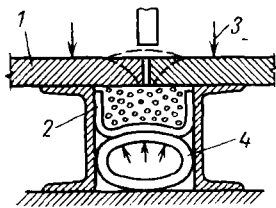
Схема сварки листов встык на флюсовой подушке
